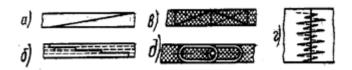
Соединение ремней: а) склеивание по косому срезу; б) склеивание по ступенчатой поверхности; в), г) сшивка встык жильными струнами; д) сшивка проволочными спиралями.
